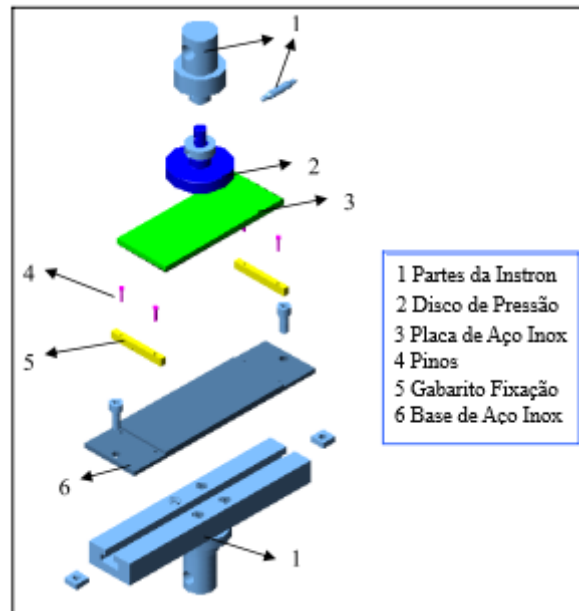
Projeto do sistema de moldagem por pressão adaptado por [39] da máquina 5582 Instron.
